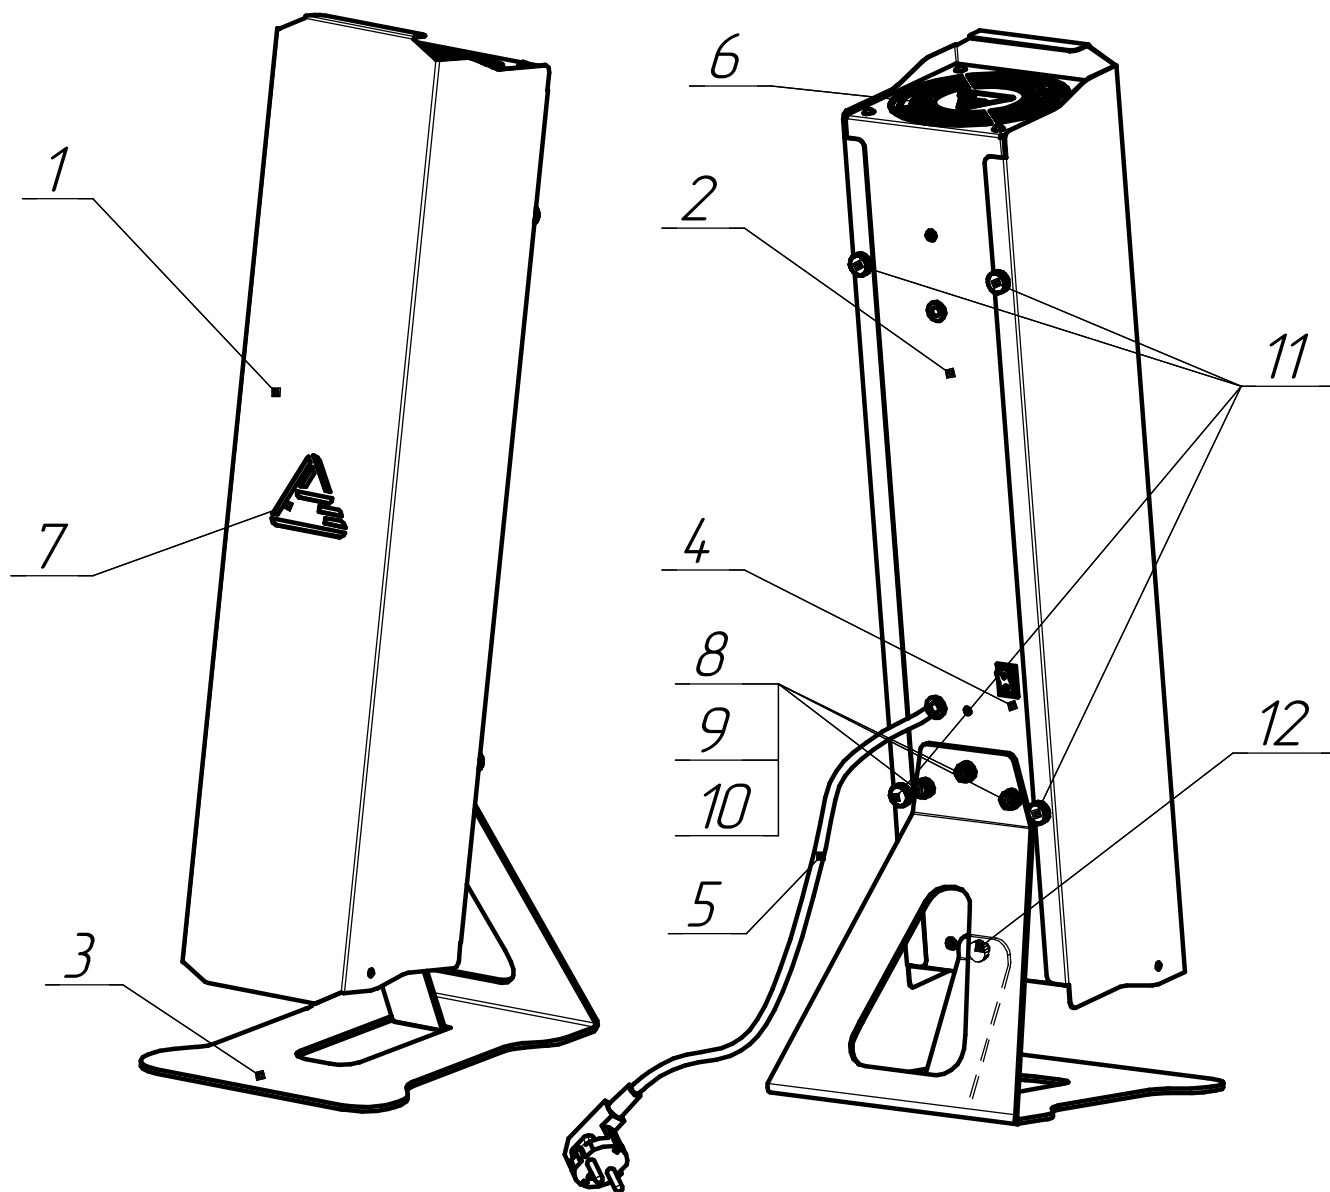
Общий вид рециркулятора ОБРН02.
